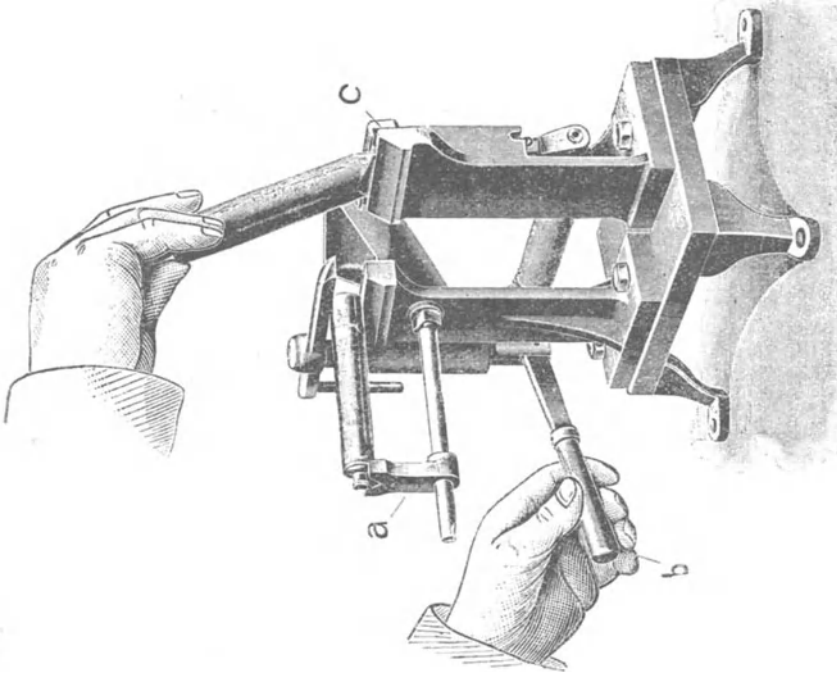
Tubenverschließmaschine für Handbetrieb.
